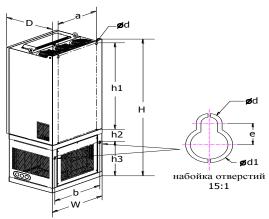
Размер G3 132 ~400 kW(с основанием реактора постоянного тока) габарит настила
